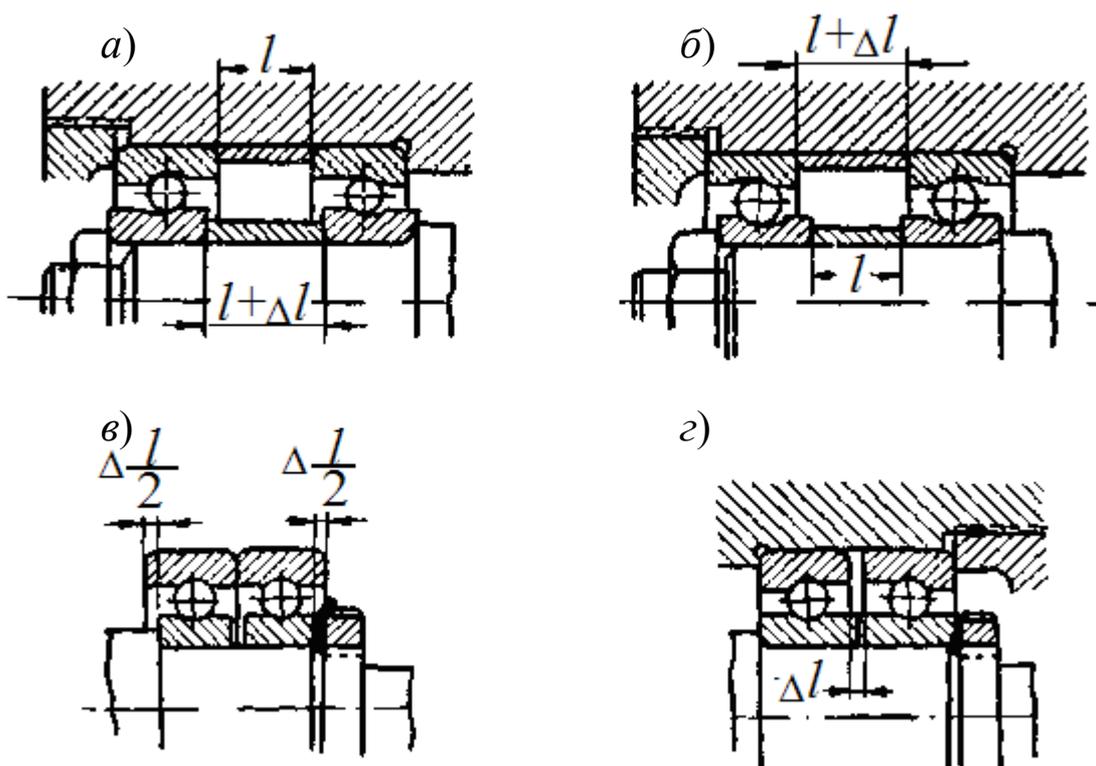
Схема монтажа подшипников с предварительным натягом
